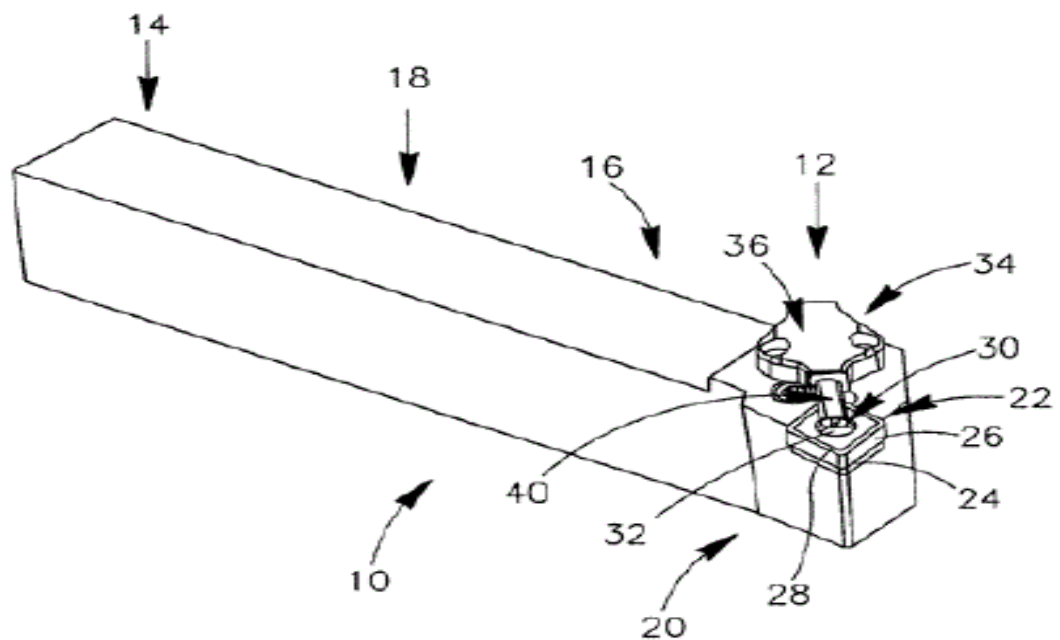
Ріжучий інструмент з подачею МОР.[16]
